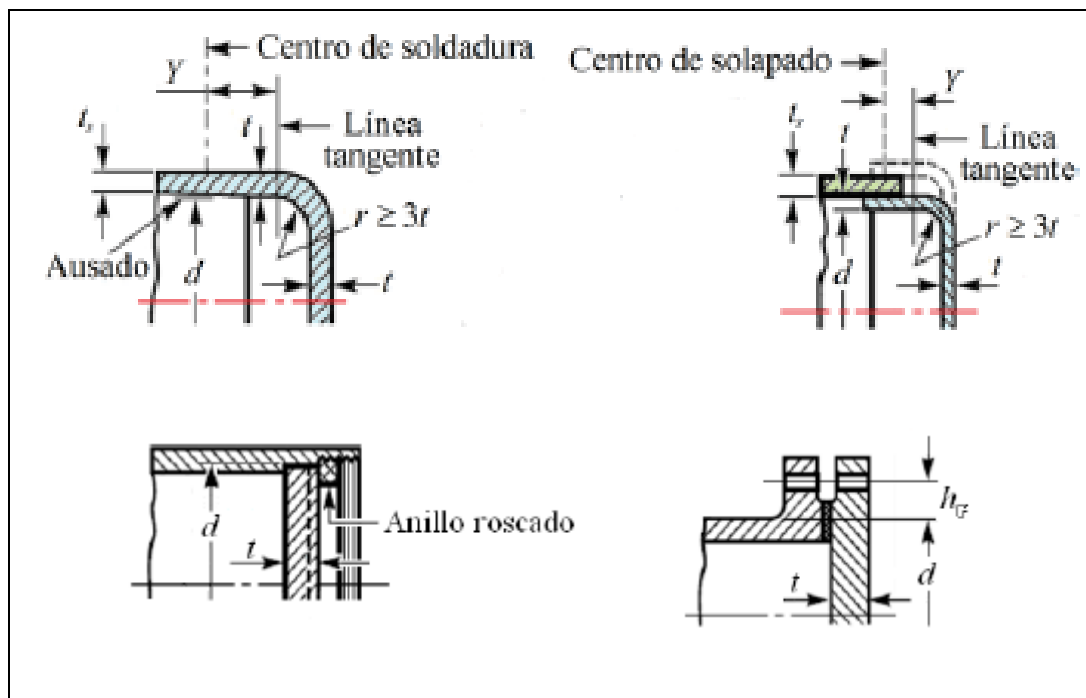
Ejemplos de soldadura cabezal plano.
